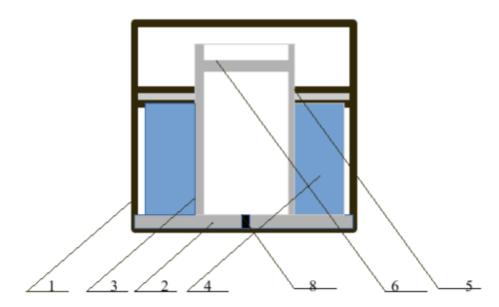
Форма мусорного ведра для сбора и уплотнения горючей фракции ТБО
